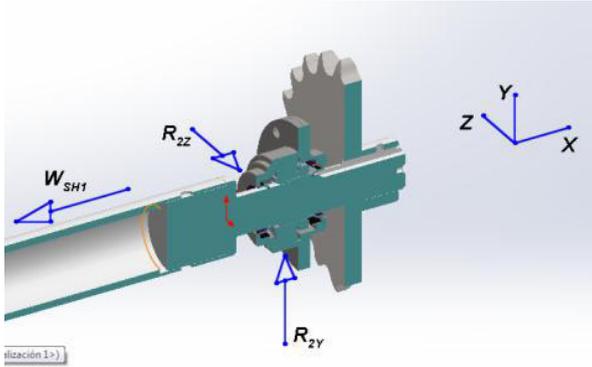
Fuerzas sobre el rodamiento delantero.
